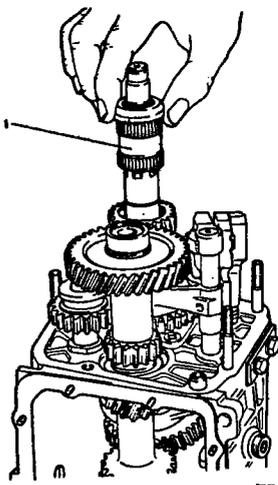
Снятие втулки шестерни V передачи: 1 - втулка
